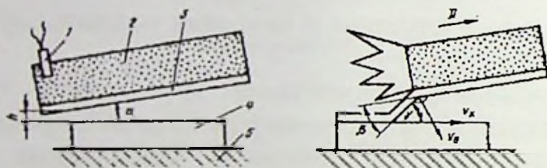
Схема сварки взрывом под углом:
